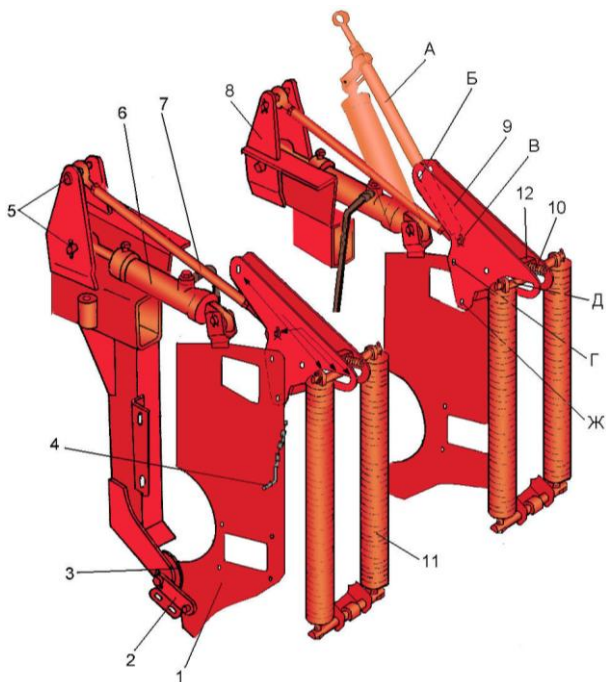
Механизм вывешивания: 1 – ловитель рамы измельчителя; 2 – накладка; 3 – ролик; 4 – фиксатор транспортного положения; 5 – пальцы; 6 – гидроцилиндр; 7 – тяга; 8 – кронштейн; 9 – рычаг механизма вывешивания; 10 – регулировочный болт; 11 – пружина; 12 – серьга; А – положение гидроцилиндров и тяг; В, В, Г, Д, Ж – отверстия рычагов механизма вывешивания
